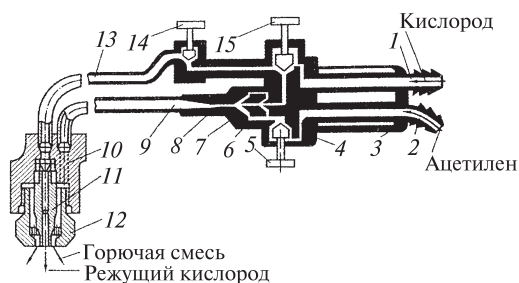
Схема универсального инжекторного резака «Факел»:
